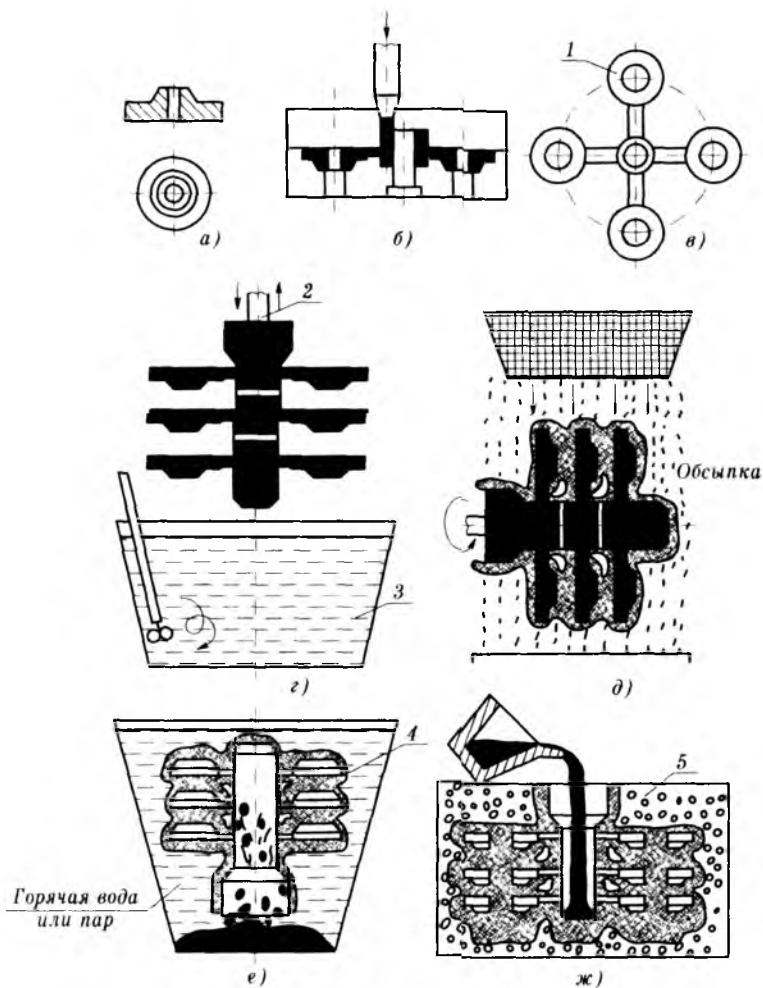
Схема изготовления формы по выплавляемой модели:
